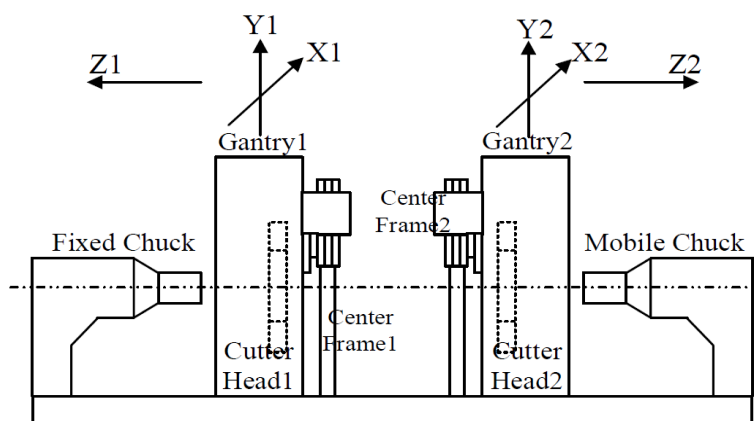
Фрезерний верстат для шліфування колінчастого вала [19]
